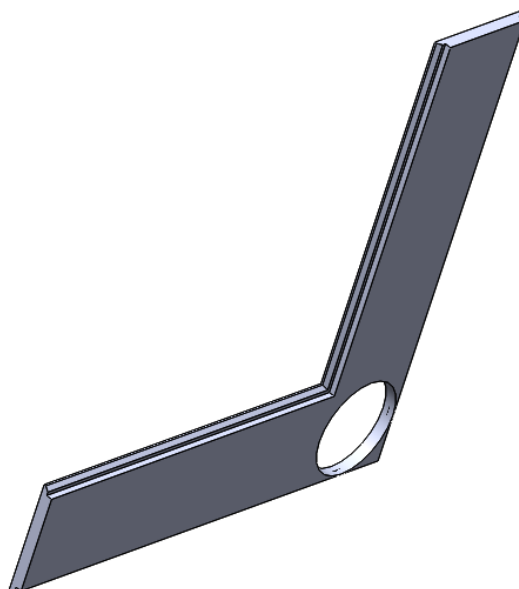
Chapa de reforço com chanfro para soldadura.
